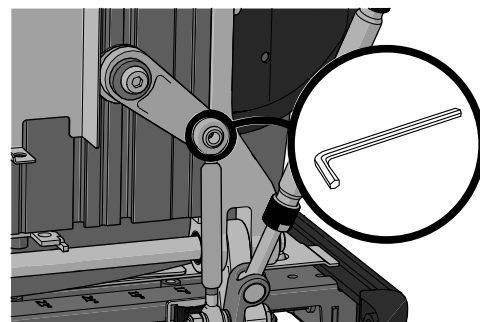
Das Gelenk für die Schiebefunktion der Rückenlehne ist mit einer Schraube befestigt.
